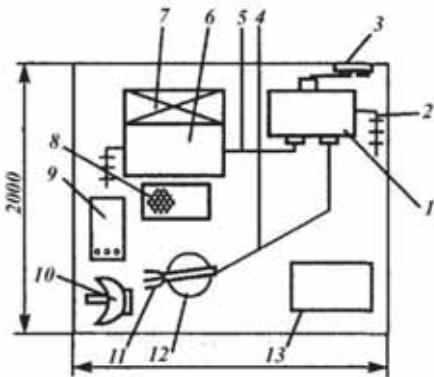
Планировка сварочной кабины: 1 – источник питания дуги; 2 – заземление; 3 – пуск источника питания дуги; 4 – прямой провод; 5 – обратный провод; 6 – стол; 7 – вентиляция; 8 – коврик; 9 – электроды; 10 – щиток; 11 – держатель; 12 – стул; 13 – ящик для отходов
